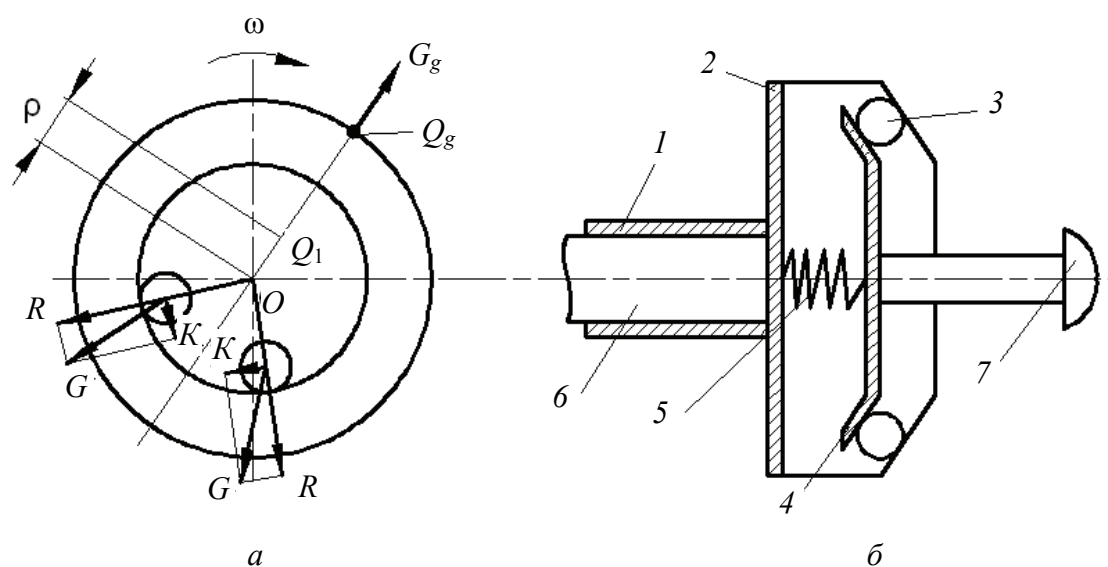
Схемы станка с балансировочными шарами и балансировочной головки
